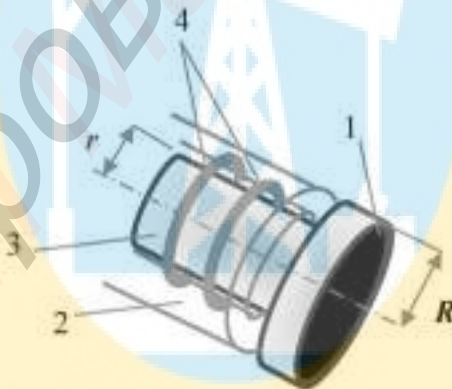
Конструкція обертаються навколо свого центру різців типу PDC:
